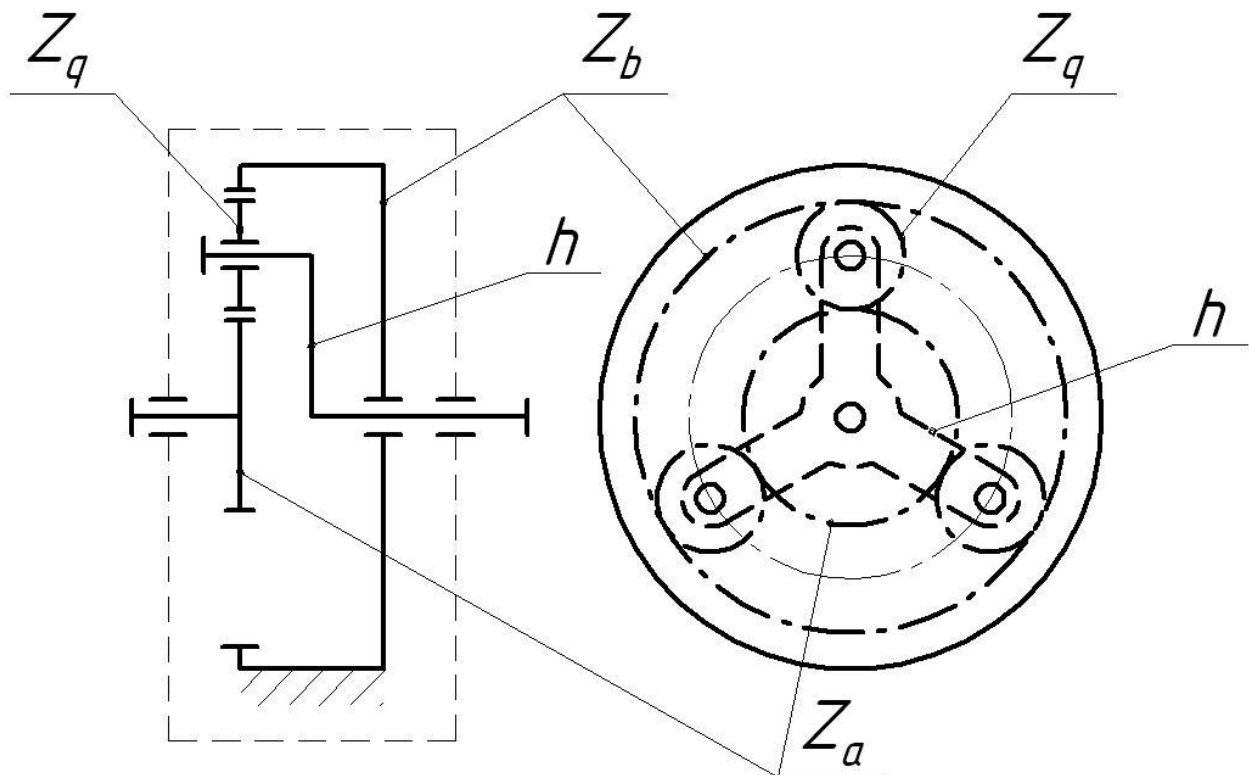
Схема планетарної передачі з одинарними сателітами
